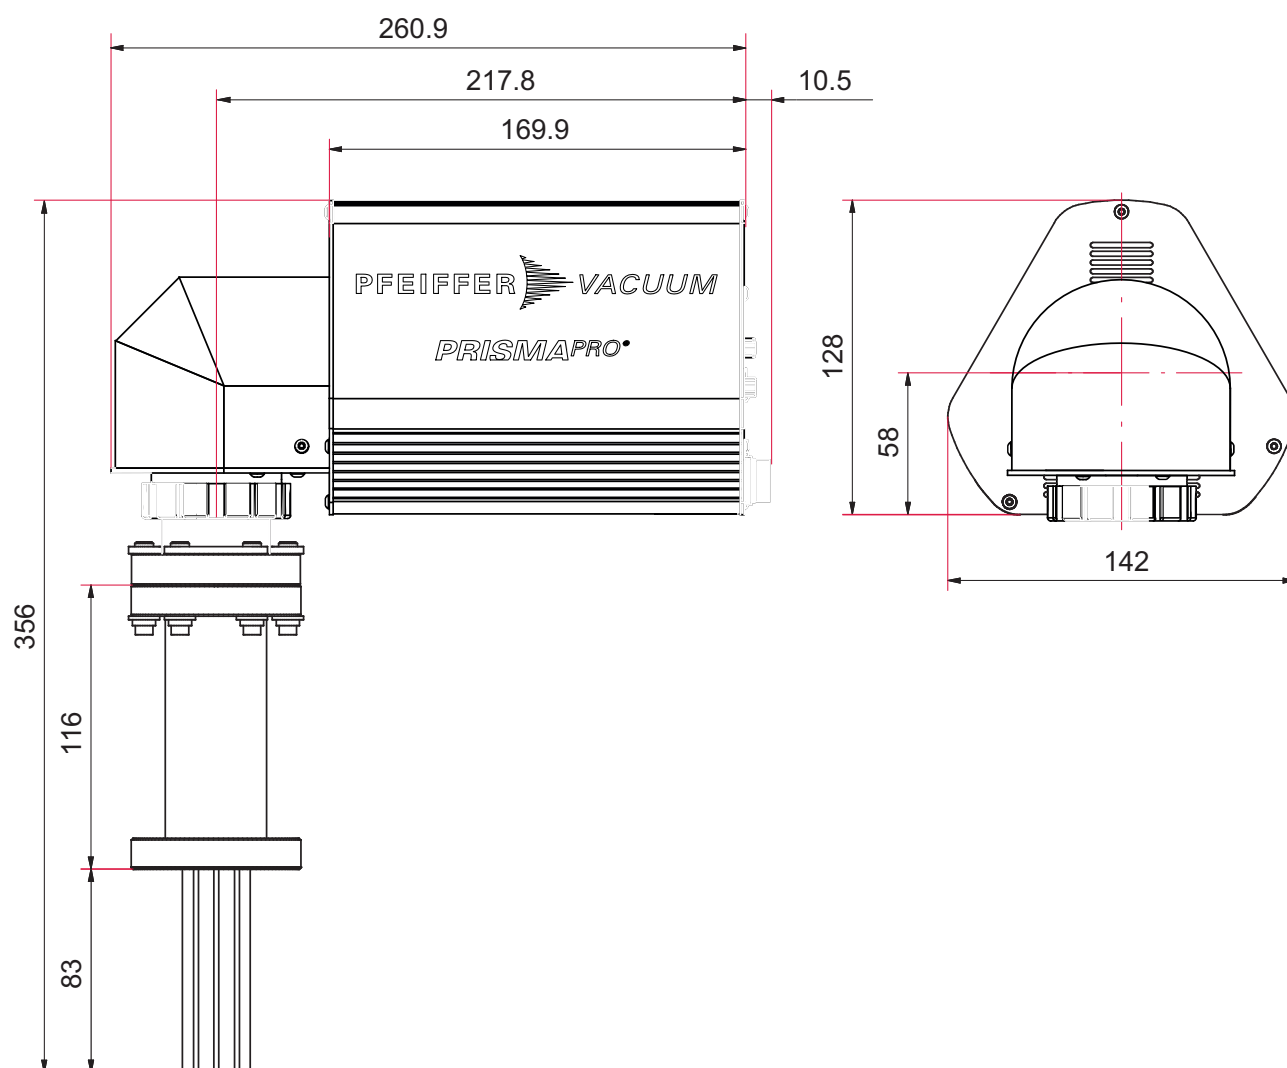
Dimensions QMG 250 M / SI ouverte / QME 250 90°
